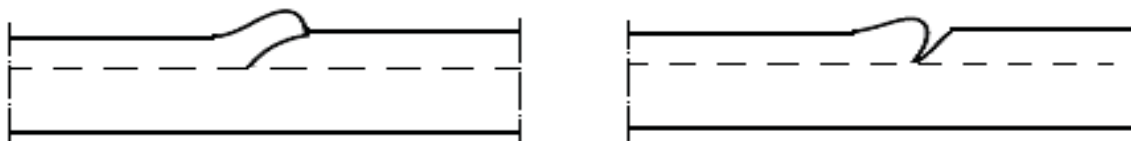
Схематичное изображение неравномерной ширины шва
